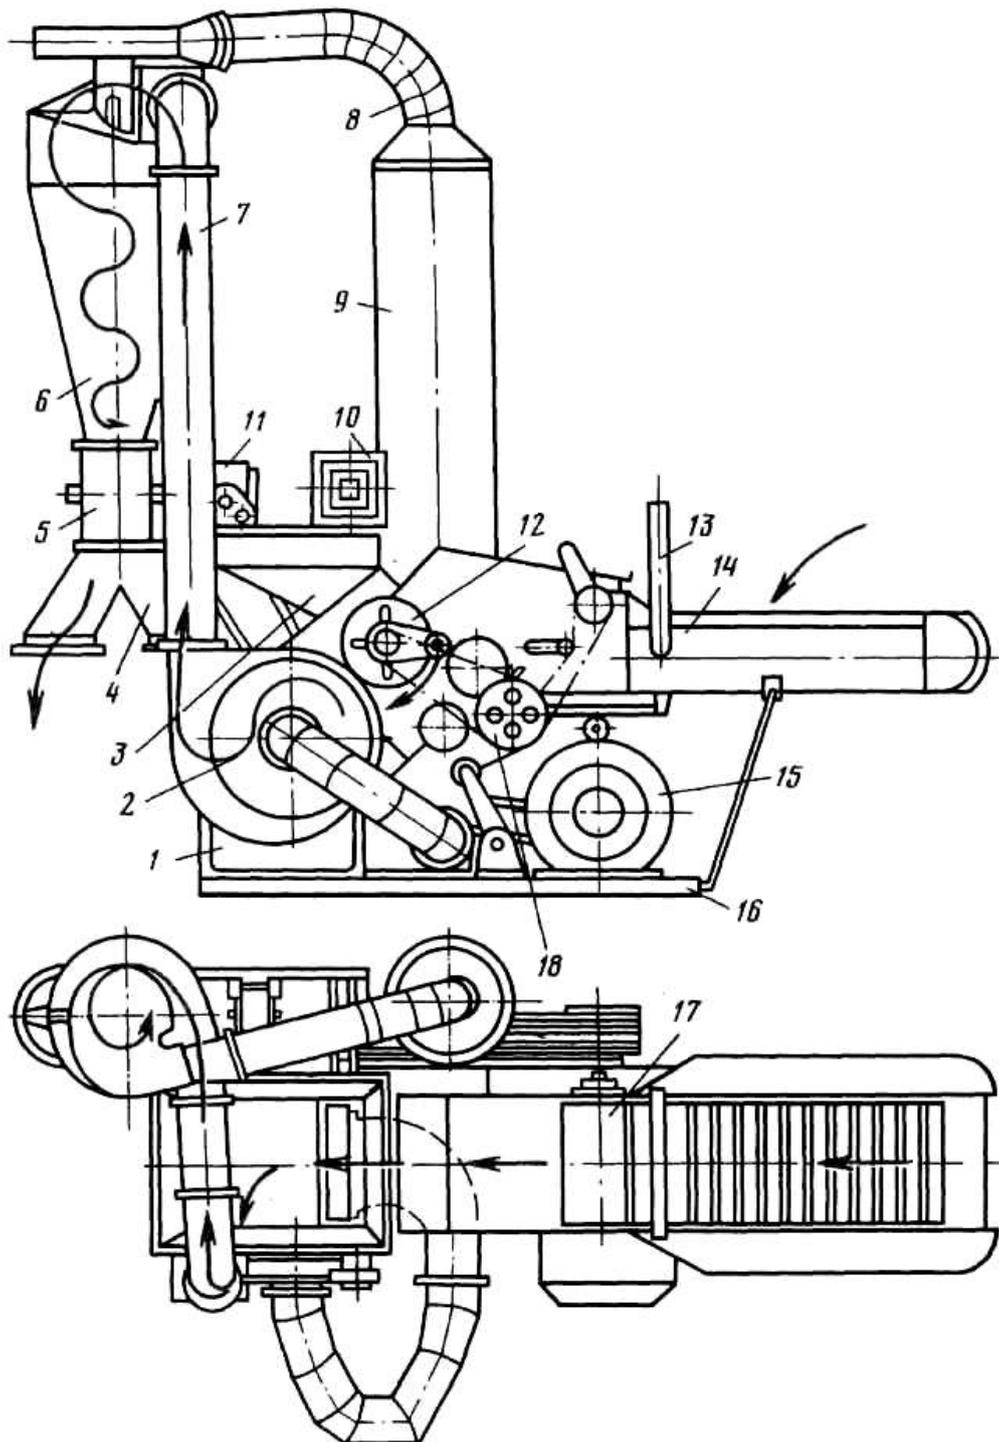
Универсальная дробилка кормов КДУ-2:
